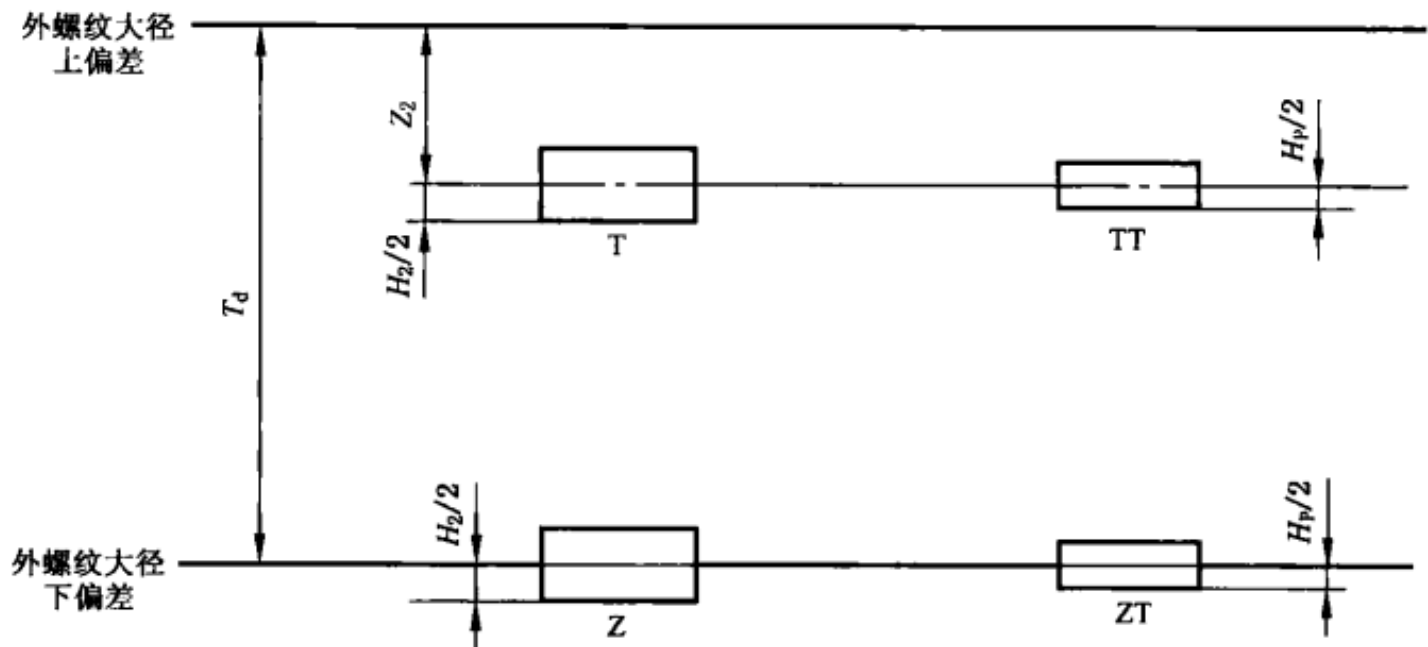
光滑环规或卡规直径的公差带位置
